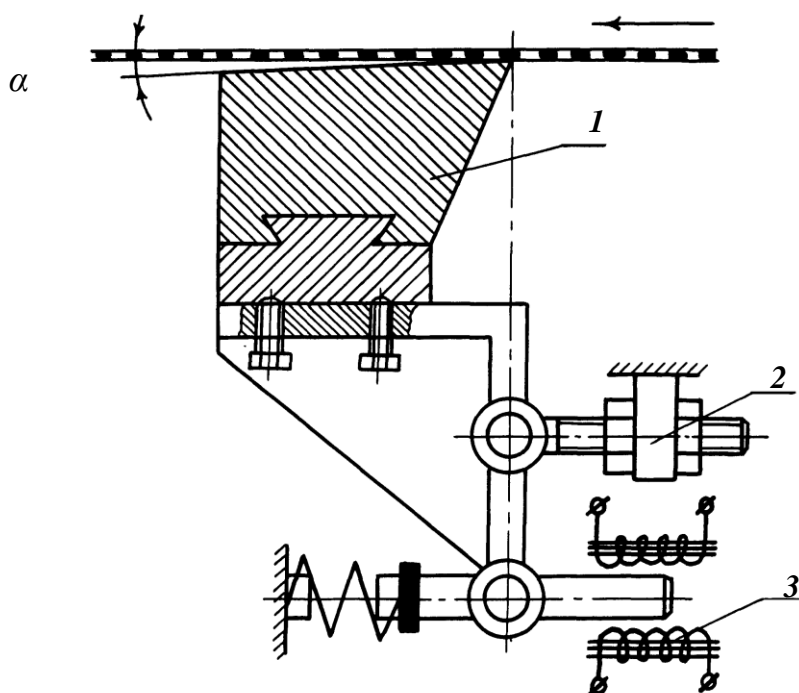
Гидропланка бумагоделательной машины по а.с.№ 1027309: 1 – гидропланка; 2 – механизм регулировки угла наклона; 3 – вибропривод
